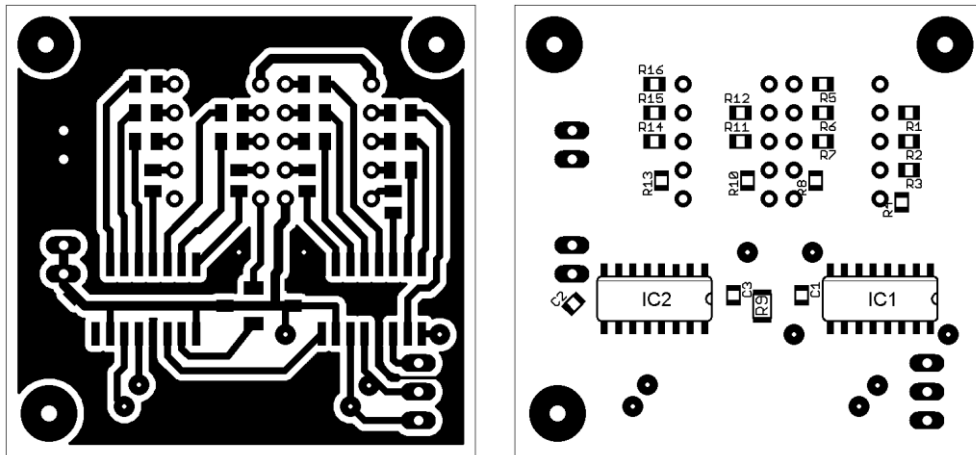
PCB digitálnej vstupnej časti a jej redukcii na panel strany „bottom“
